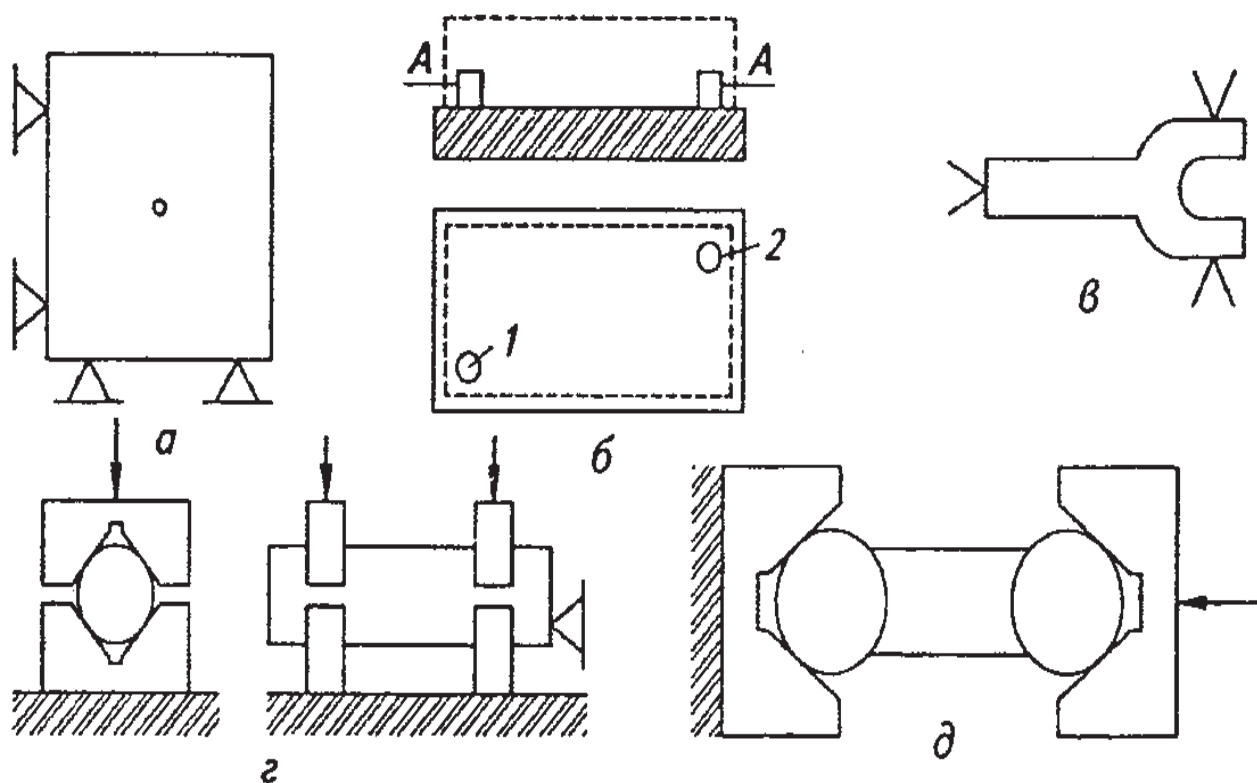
Базирование деталей при фрезеровании и сверлении: а–д – варианты; 1, 2 – шпильки
